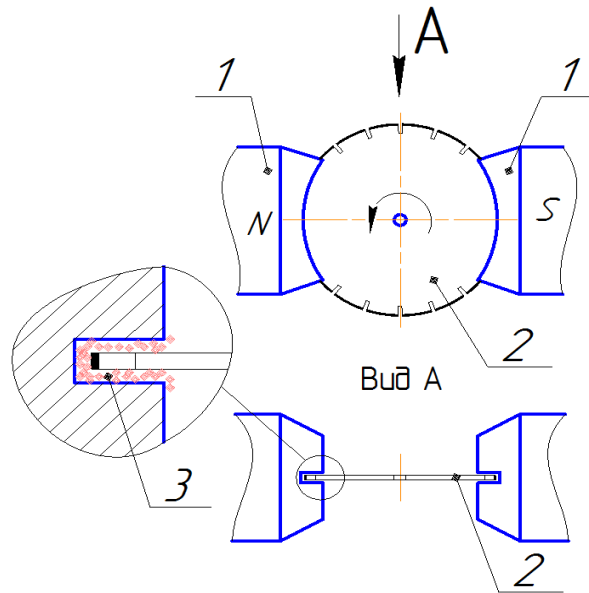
Схема установки для магнитно-абразивной правки отрезных кругов:
